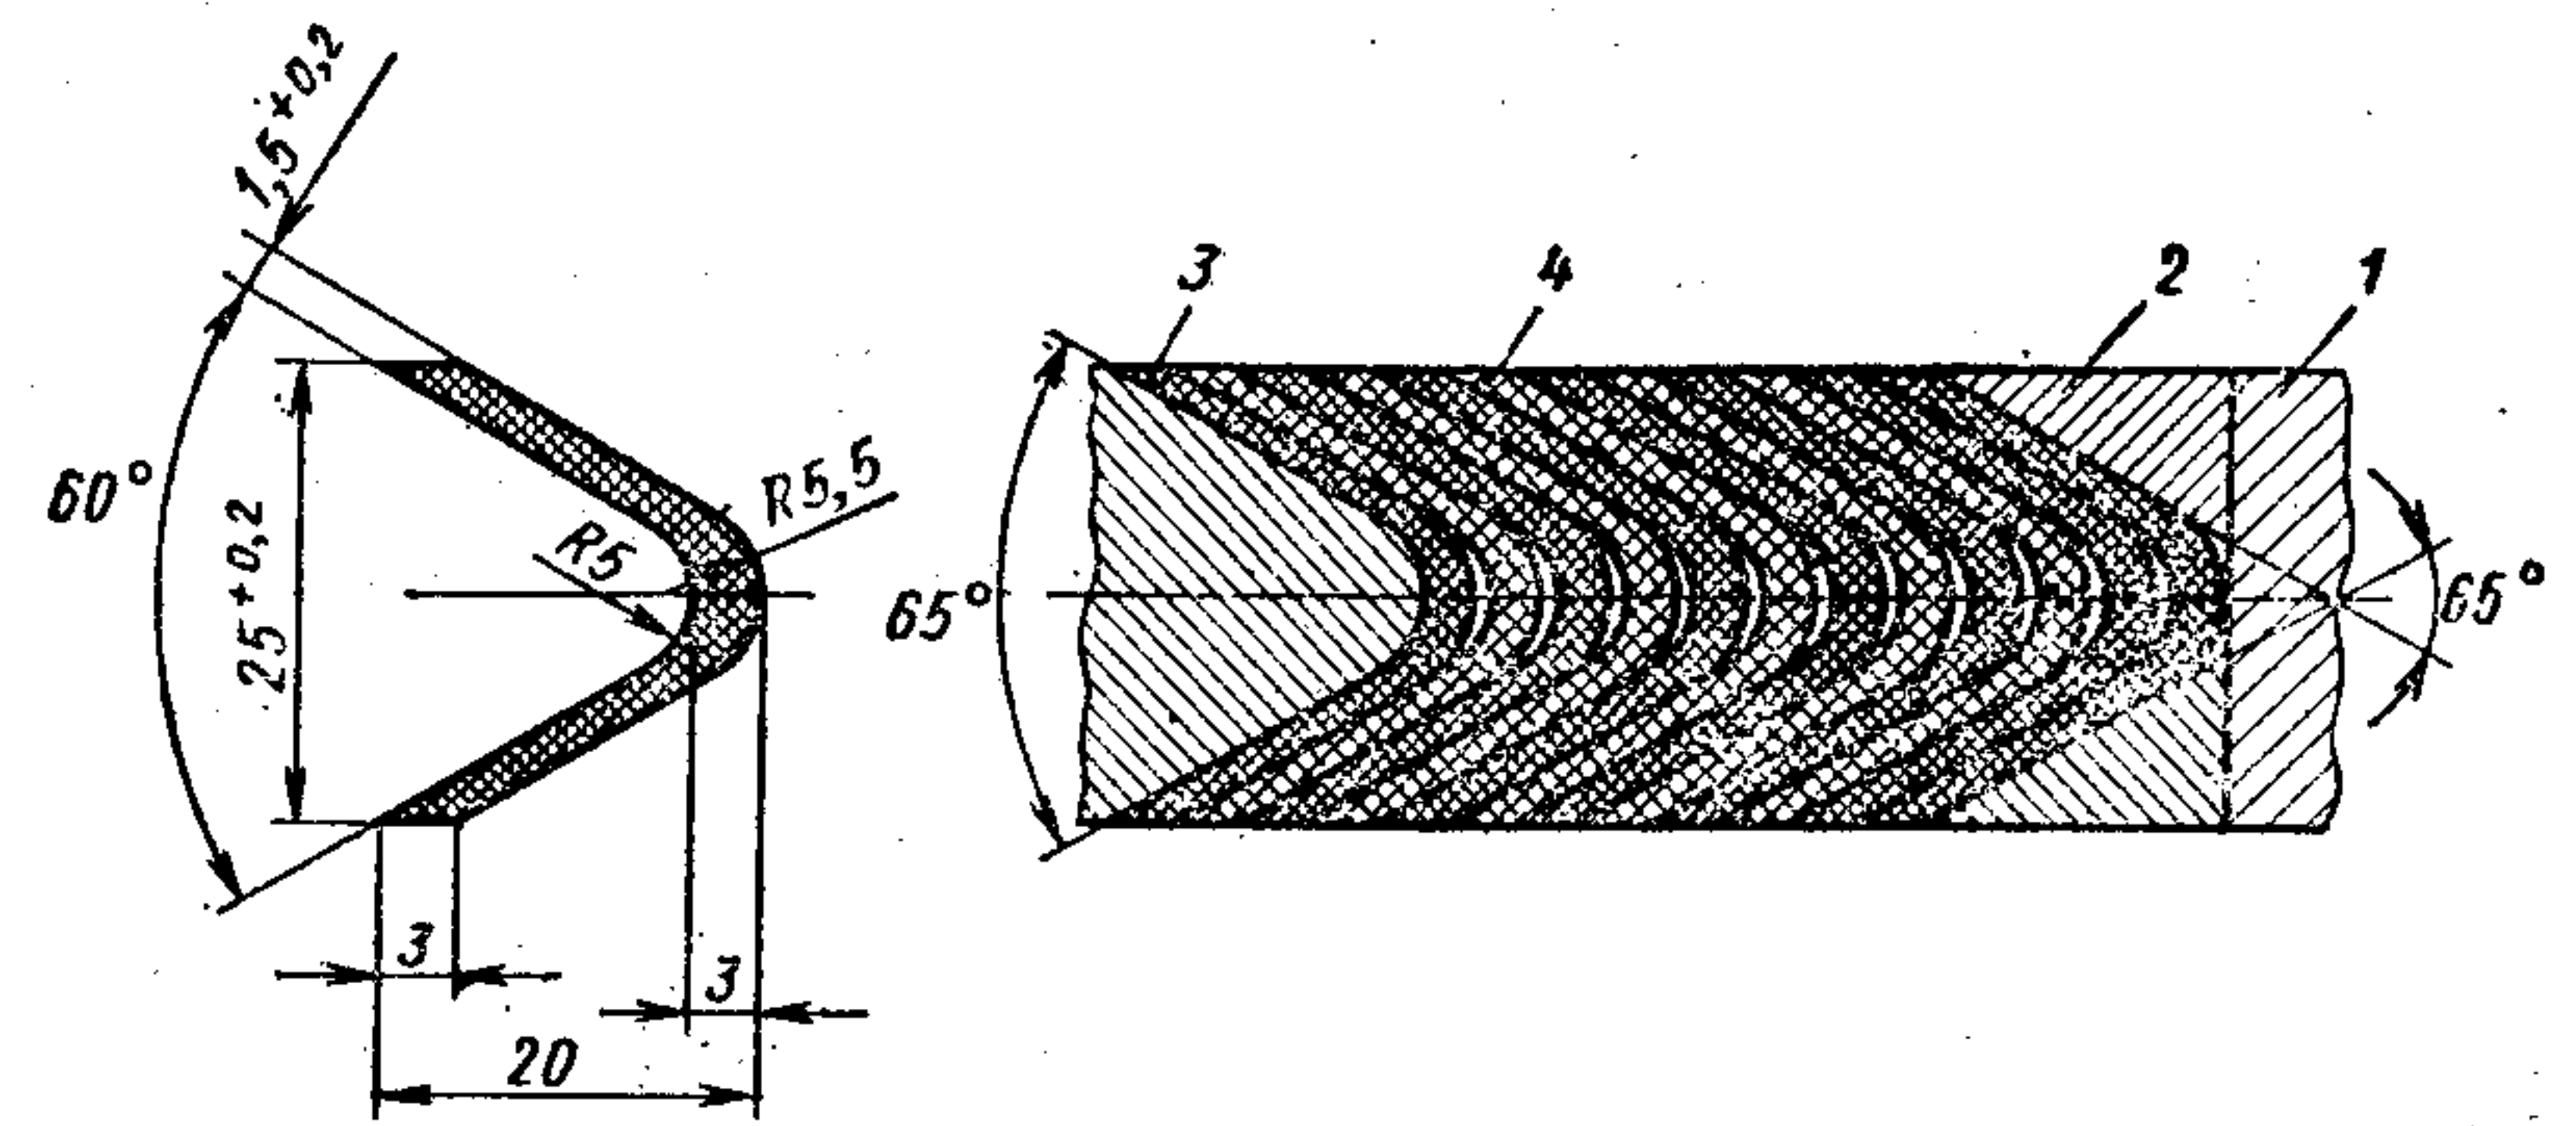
Конструкция уплотнения одноплунжерного пресса:
